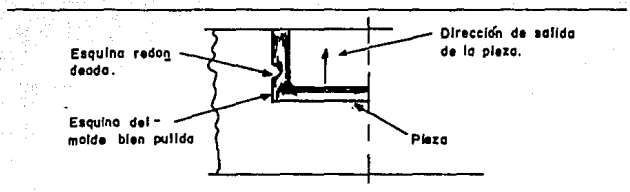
Recomendaciones para el diseño de entalladuras. (Ref. 8).
